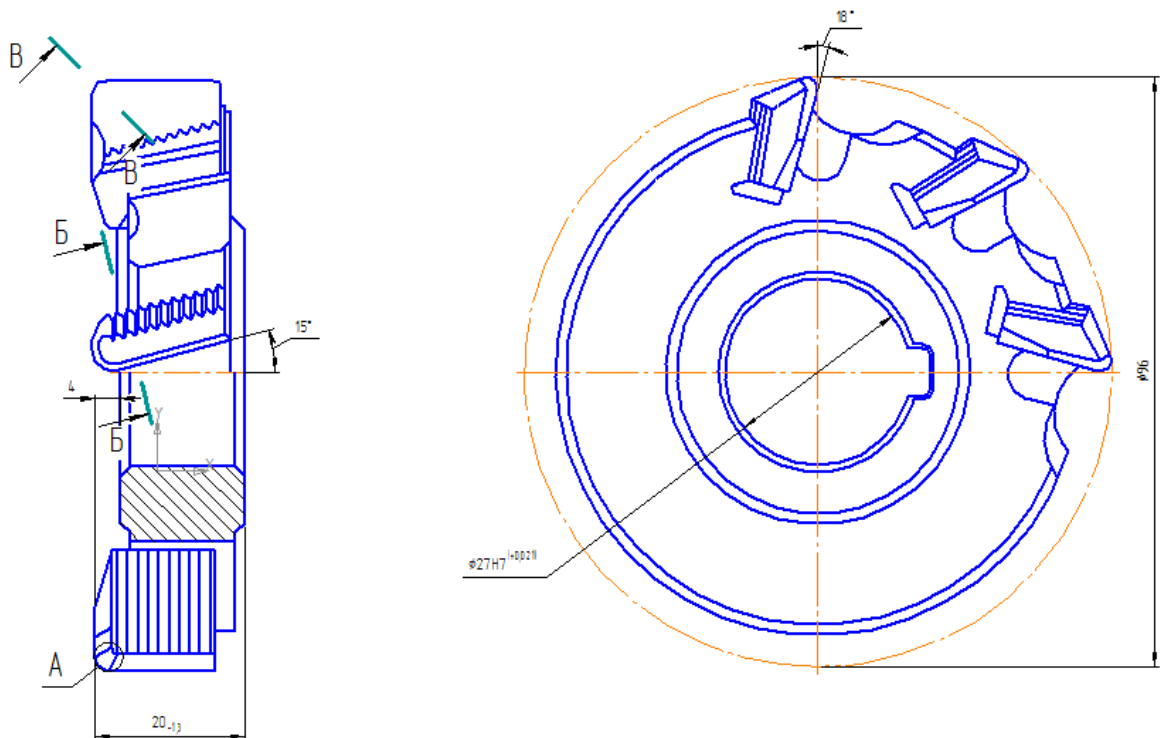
Эскиз фрезы со вставными ножами
